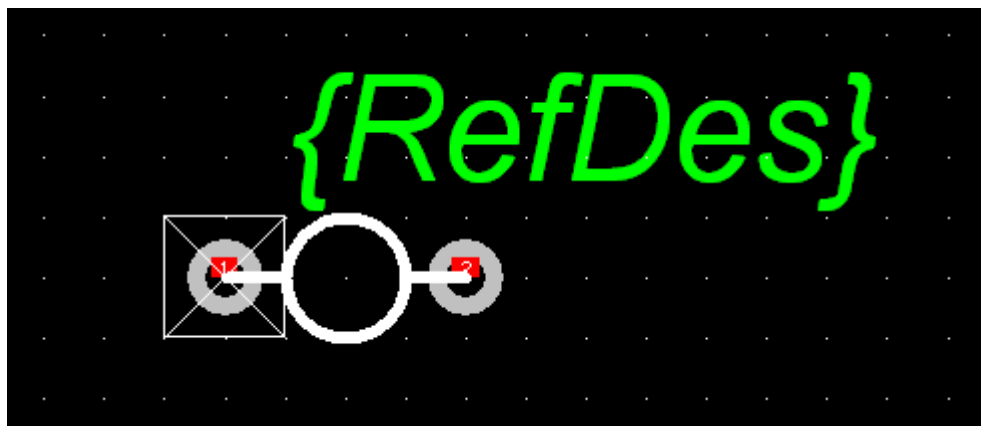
Корпус керамического конденсатора (Grid=1.25mm)
